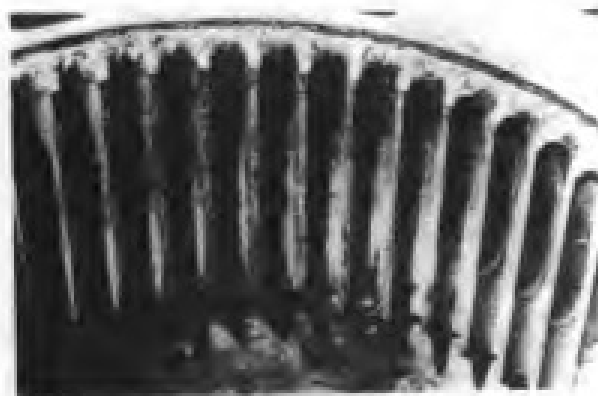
齿轮联轴器内齿轮的微动腐蚀
